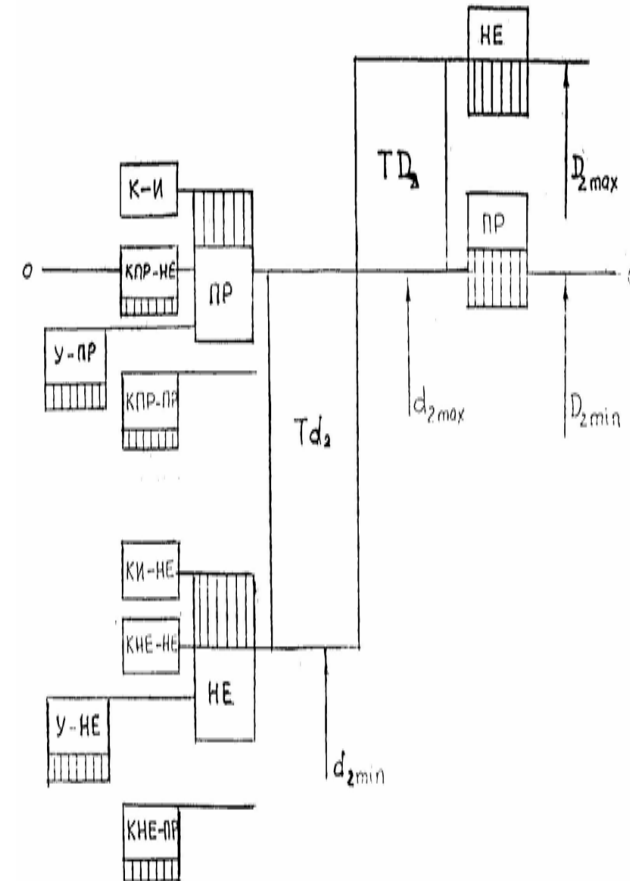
Схема расположения полей допусков резьбовых калибров
